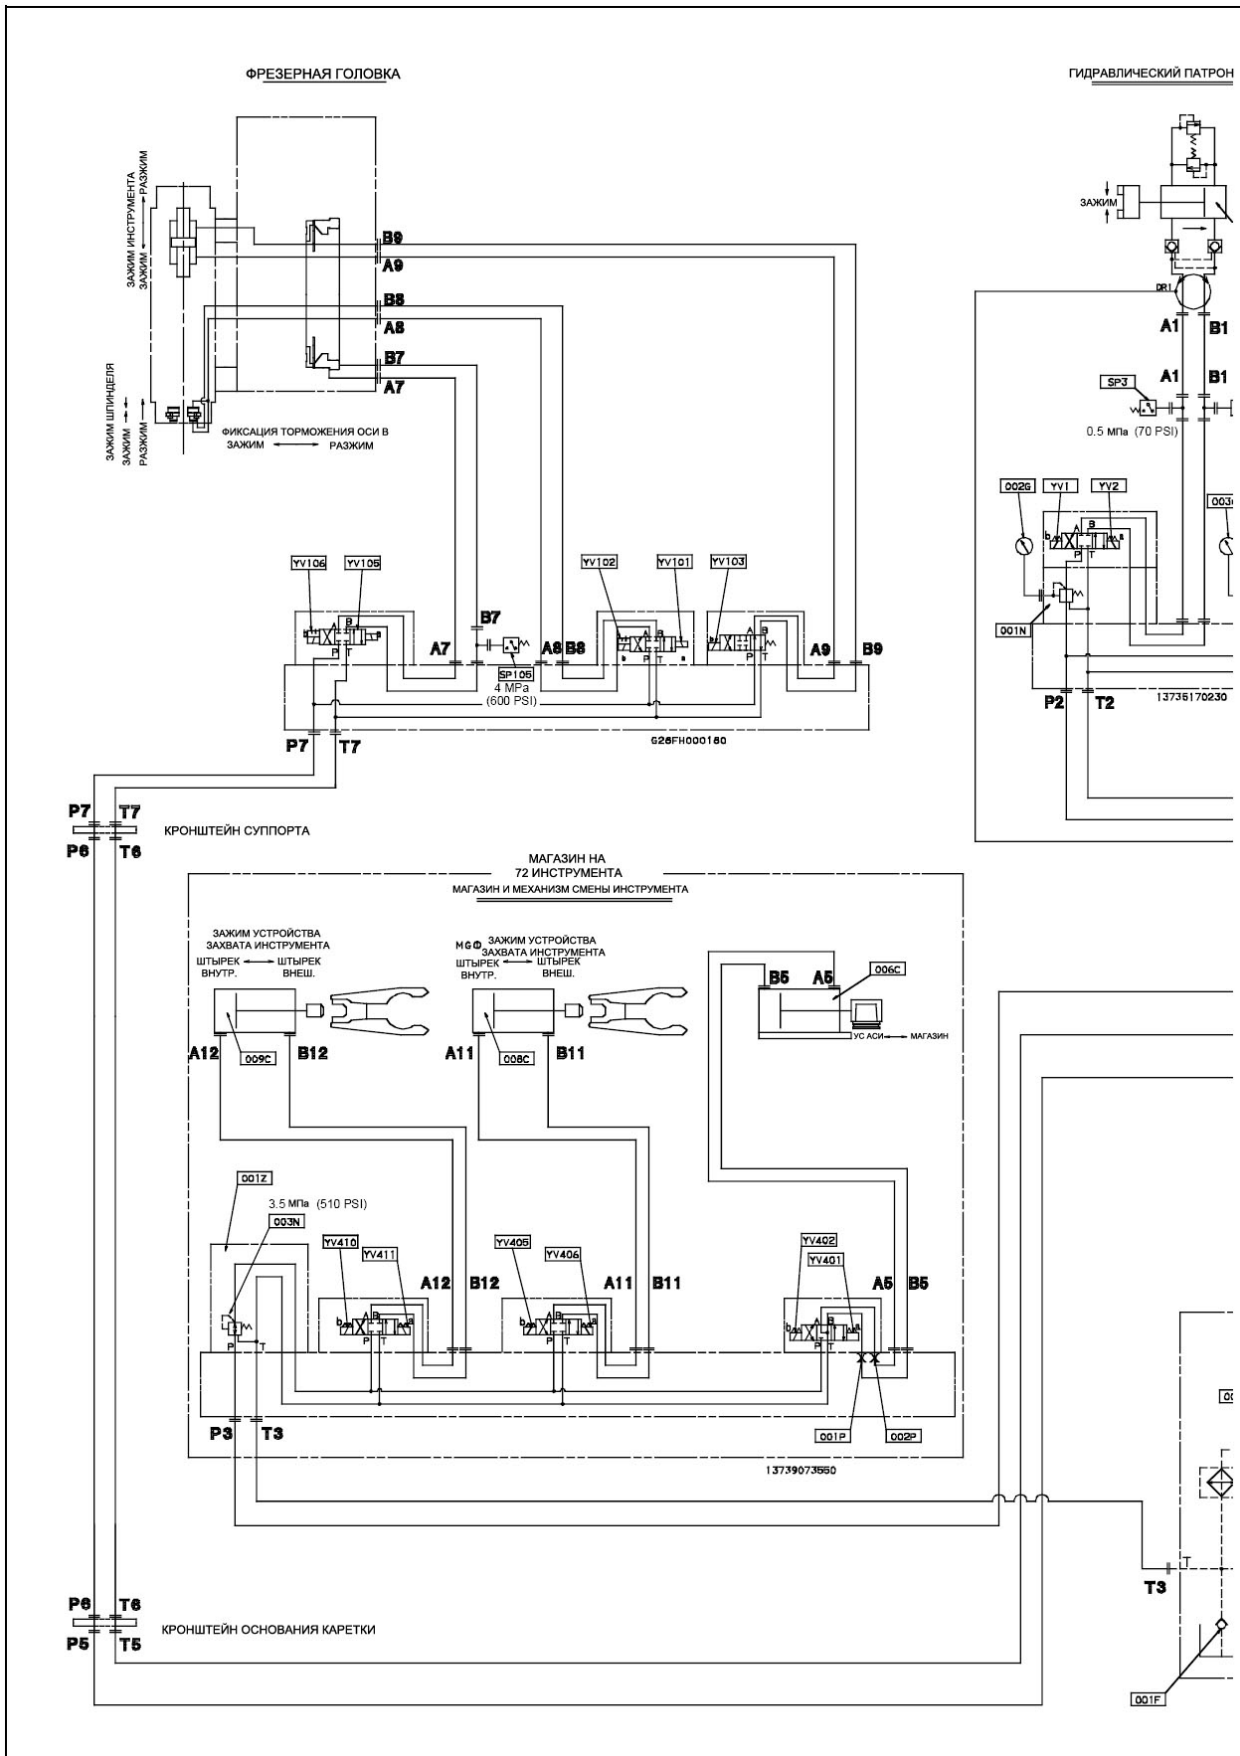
Схема гидравлического контура (магазин на 72 инструмента)
